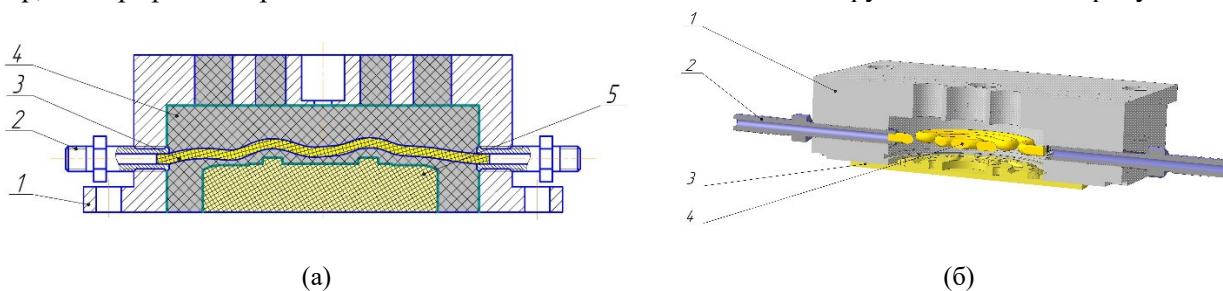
Схема композитной пресс-формы, продольный разрез (а):
